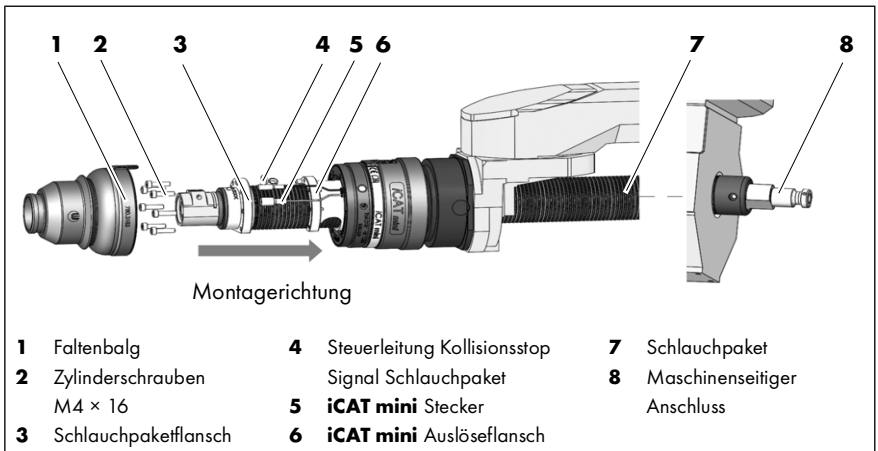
Schlauchpaket montieren iCAT mini für ABIROB® G
